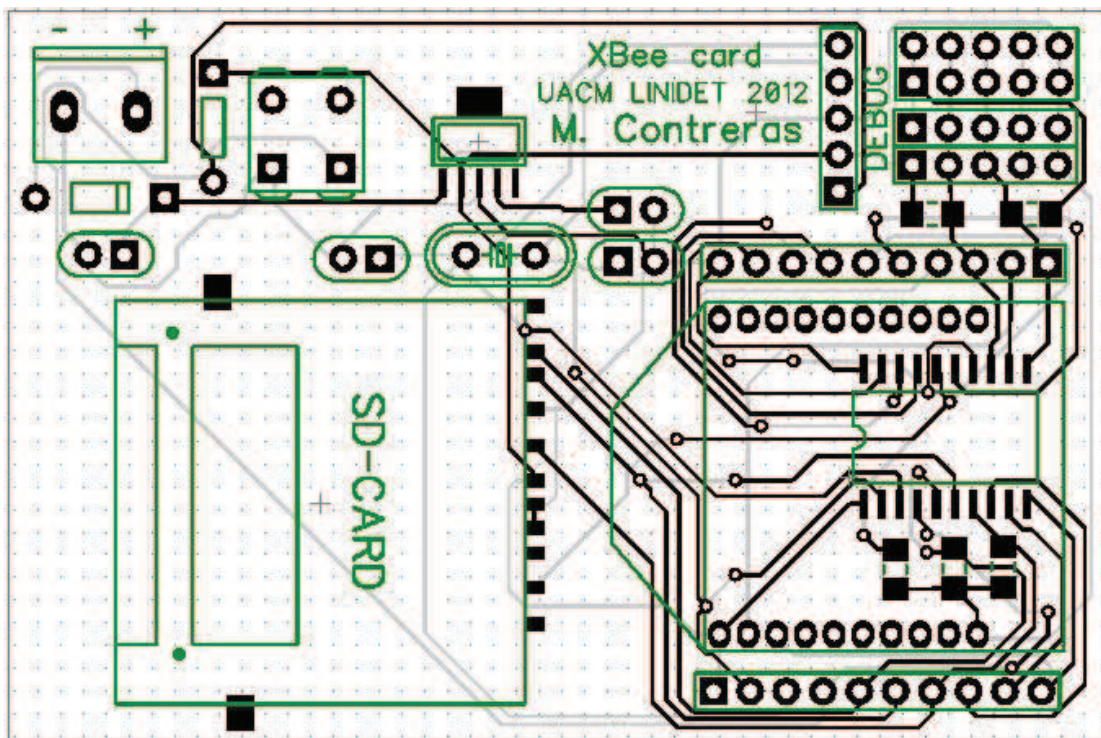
Tarjeta PCB del nodo sensor modificada
